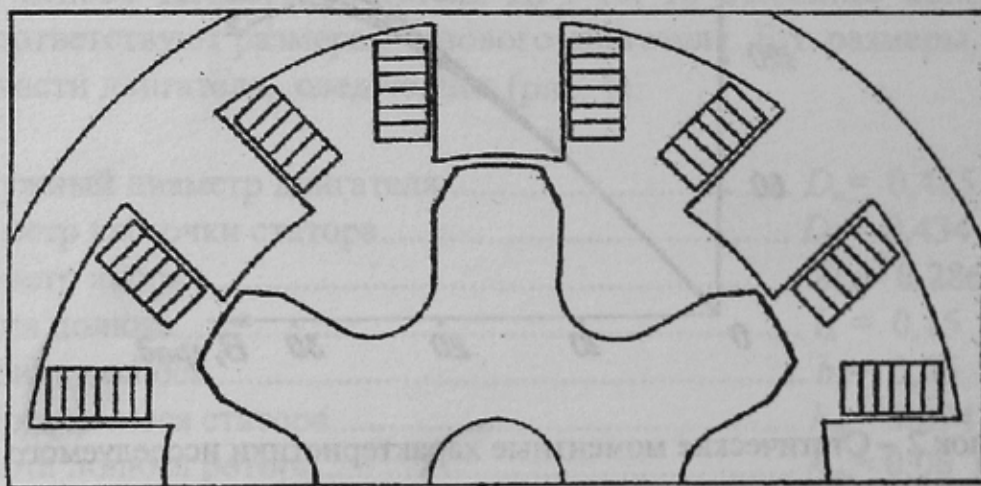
Схема конструкции разработанного двигателя с трапециевидными стенками полюсов ротора вблизи воздушного зазора
